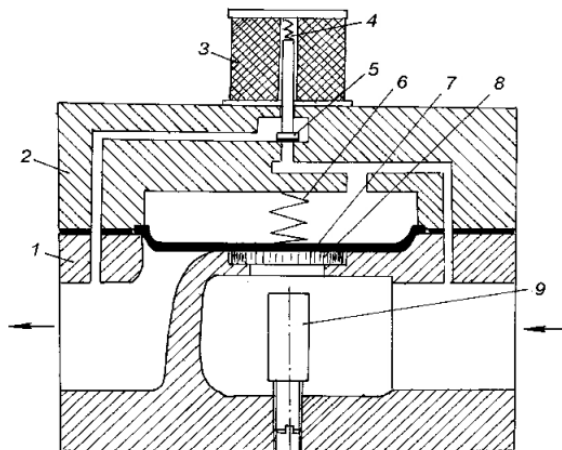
Електромагнітний виконавчий механізм: 1 – нижній корпус; 2 – верхній корпус; 3 – соленоїд; 4,6 – пружини; 5 – клапан регулюючий; 7 – мембрана; 8 клапан виконавчий; 9 – шток
